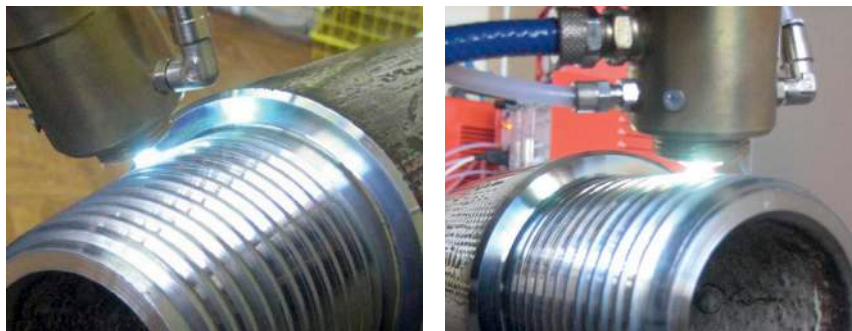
Плазменное упрочнение замковой конической резьбы
